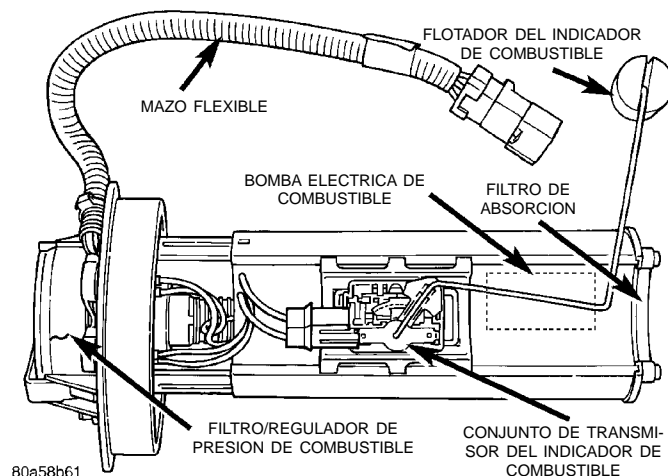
Localización del conjunto de transmisor de la bomba de combustible
